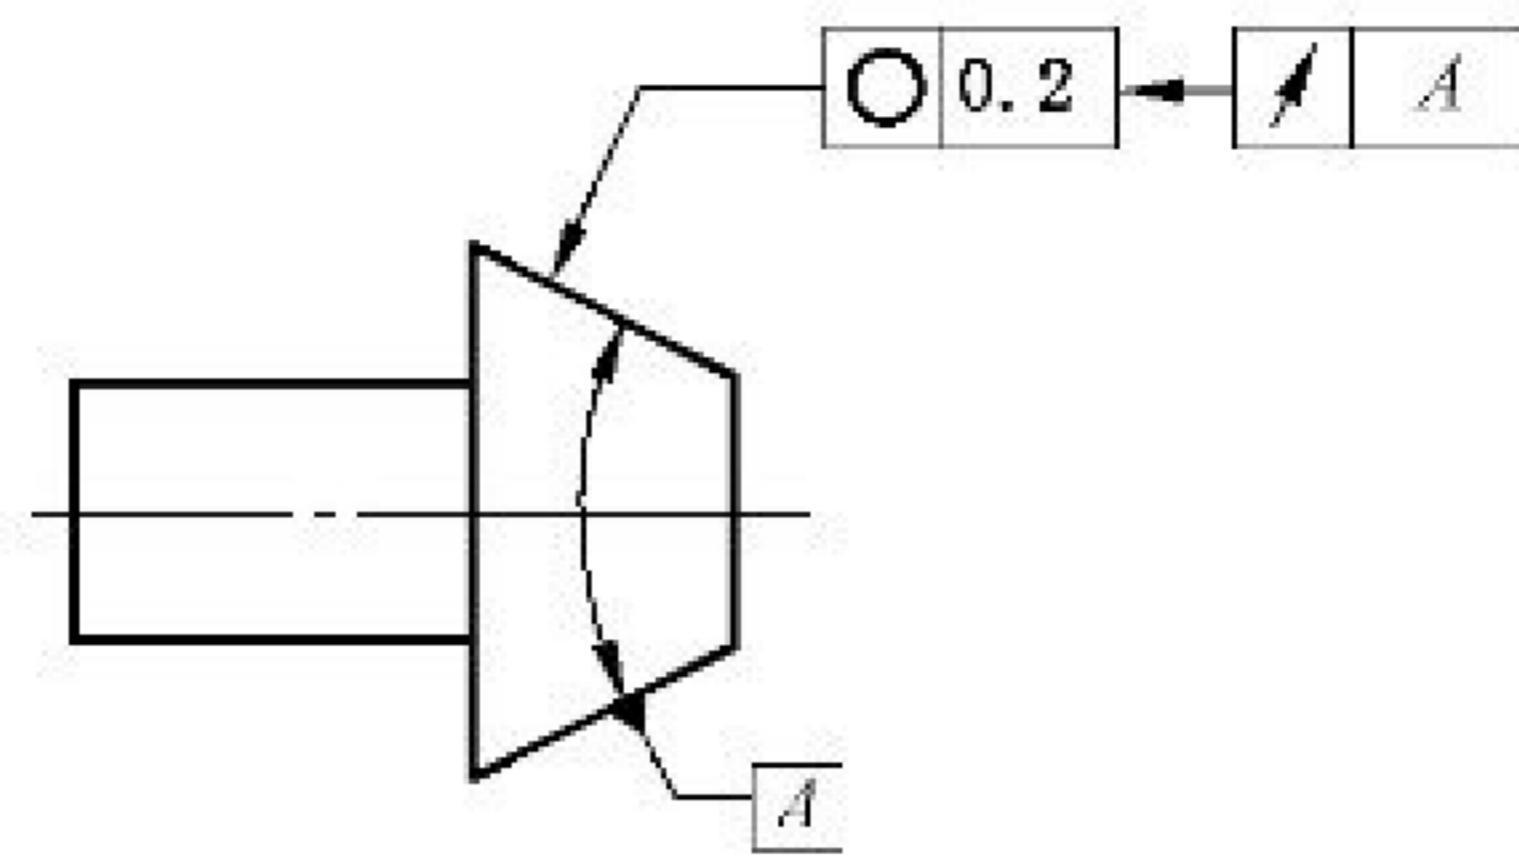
与被测要素的面要素垂直的圆度公差标注
